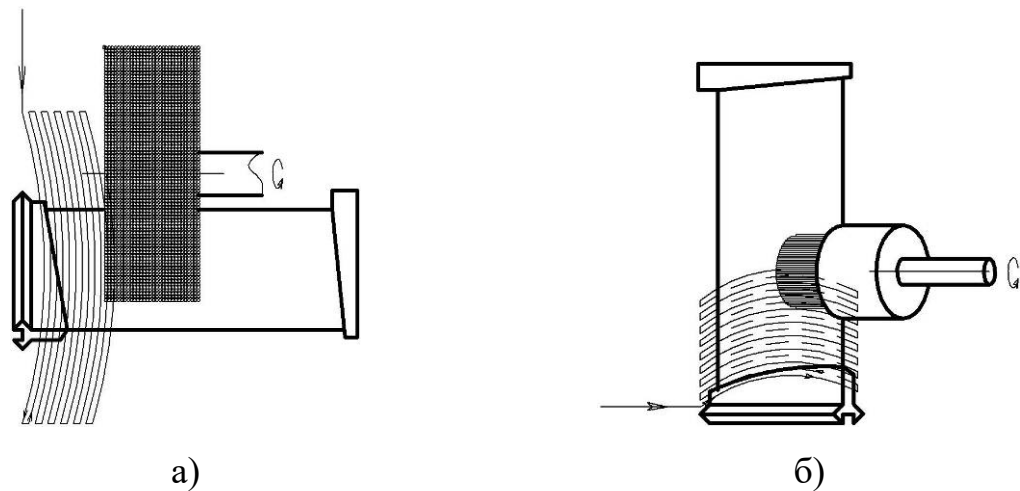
Схема обробки пера лопаток: а – дискова ПАЩ; б – кінцева ПАЩ
